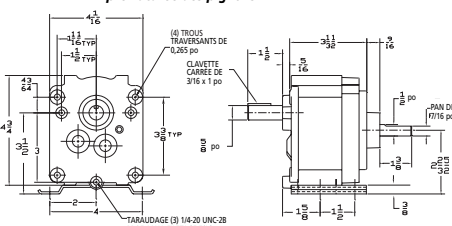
Dimensions - 2Z819A à 2Z821A et 4Z498 à 4Z503
